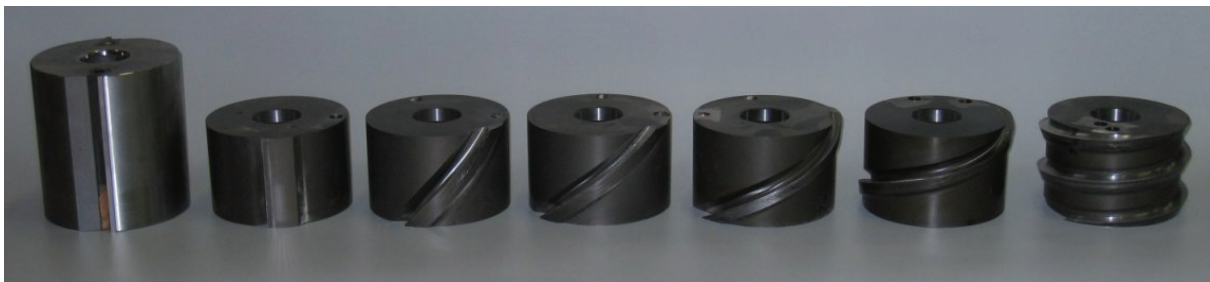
Verwendete Schraubfräser und Vergleichswerkzeuge mit Werkzeug-Neigungswinkeln λ_s von 0° bis 85°
